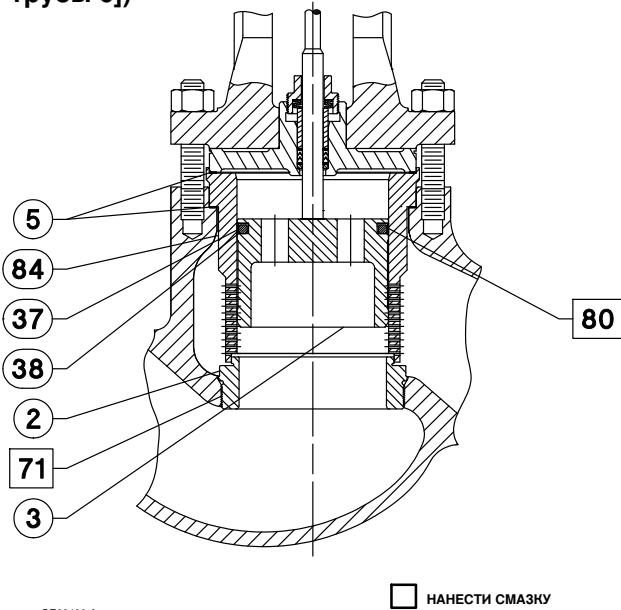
Неразруженный трим с направляющей клапана GX Fisher (стандартно для размеров от Ду 40 до 150 [номинальный размер трубы 1-1/2 до 6])
